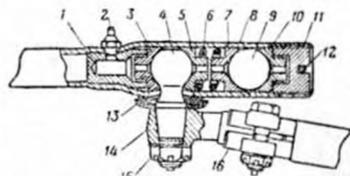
Шарнирное соединение маятникового рычага и тяги рулевой трапеции с тягой сошки: 1 — заглушка; 2 — масленка для смазки; 3, 5, 7 и 10 — сухари; 4 — палец тяги рулевой трапеции; 6 — пружина; 8 — тяга сошки; 9 — палец маятникового рычага; 11 — пробка; 12 — шпатель; 13 — уплотнитель; 14 — наконечник тяги сошки; 15 — гайка шаровой вилки; 16 — тяга сошки
